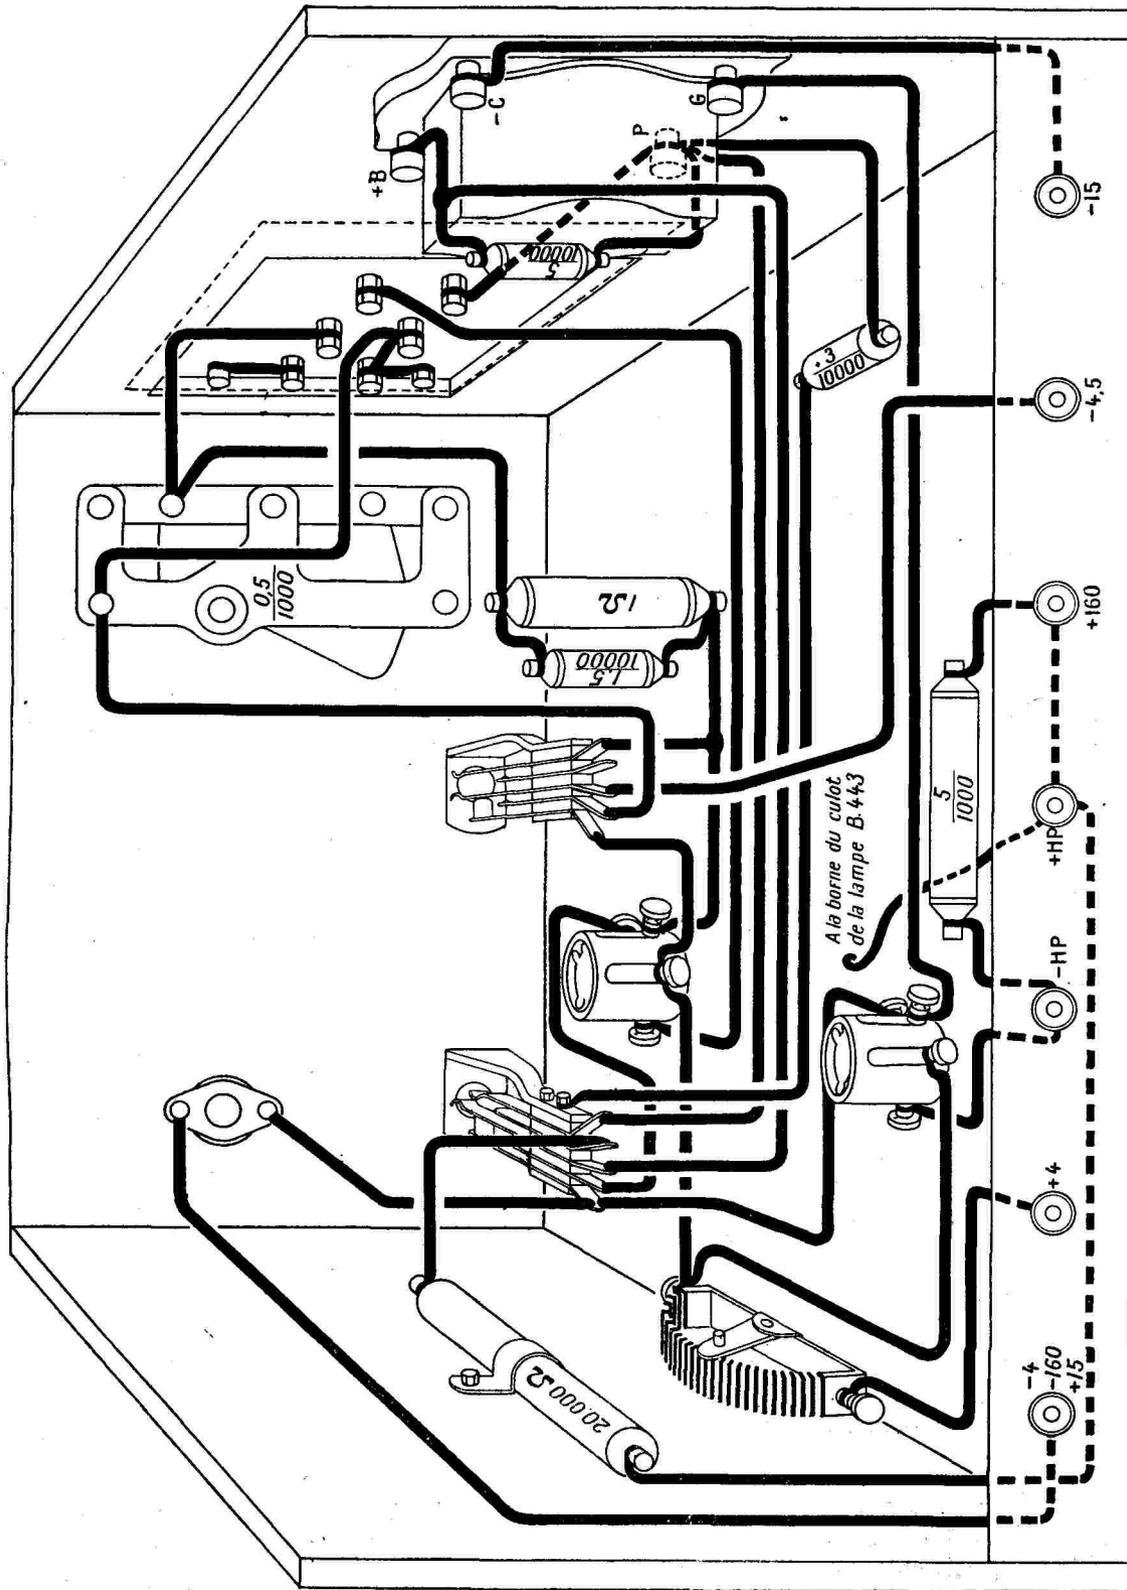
Plan de connexions de l'appareil. Les deux planches de côté ainsi que la planche de base font partie de l'ébénisterie. Dans la planche de droite est encastrée la planche en ébonite supportant les bobines.
